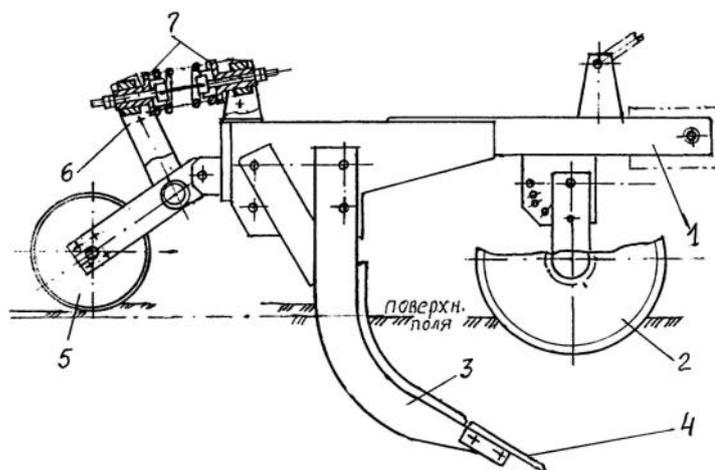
Конструктивная схема РКЛ-50 с регулировочно-предохранительным устройством.
